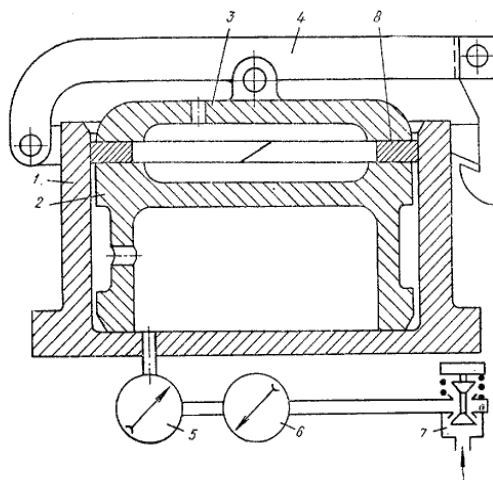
Пристрій для випробування поршневих кілець.
